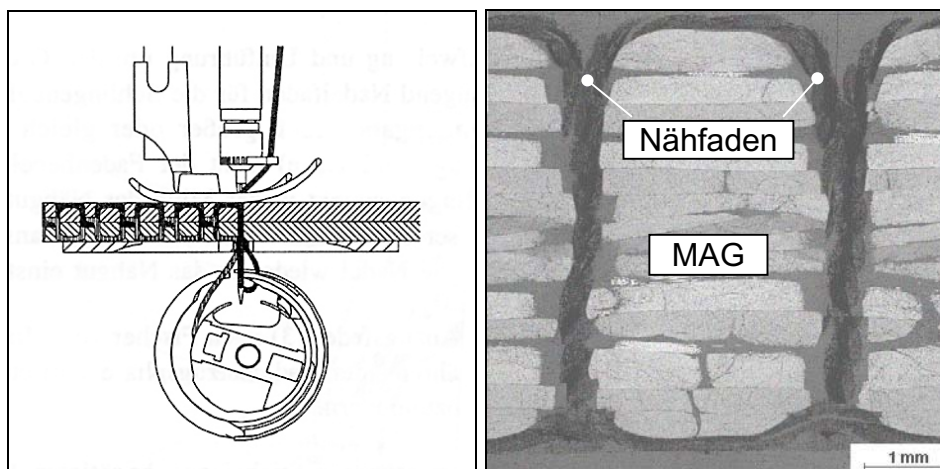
Einsatz der Nähetechnik im Preforming von Faserhalbzeugen
